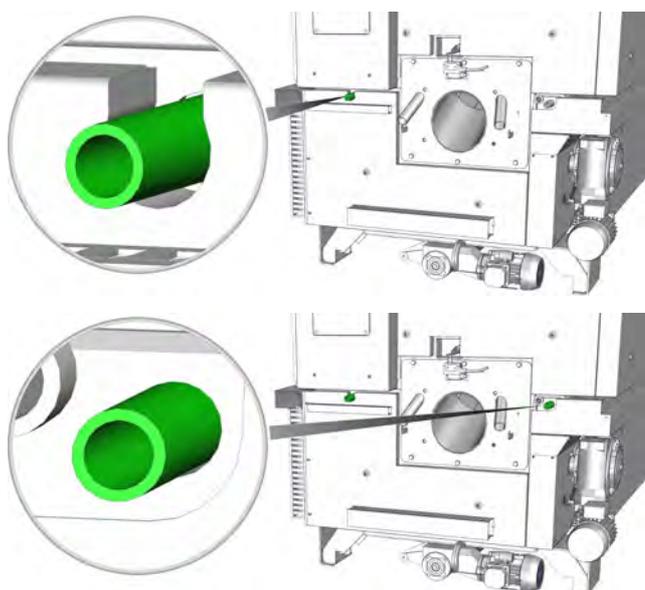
Raccords pour soupape thermique de la chambre de combustion
